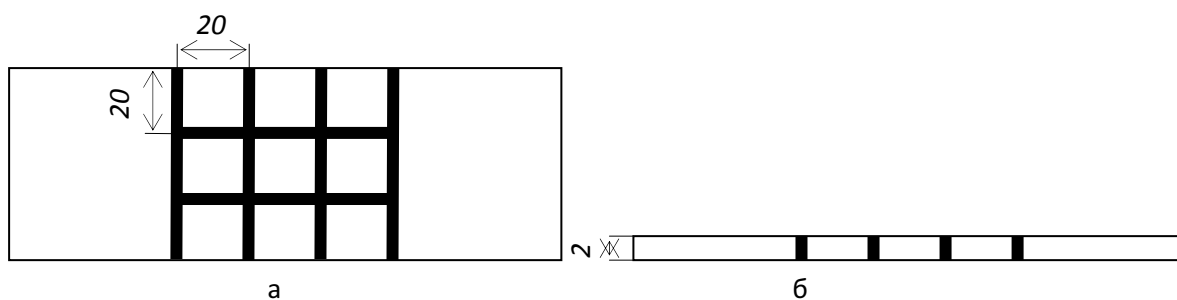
Образец с искусственным «жестким» каркасом (со сваренными квадратами): а – вид сверху; б – вид сбоку
